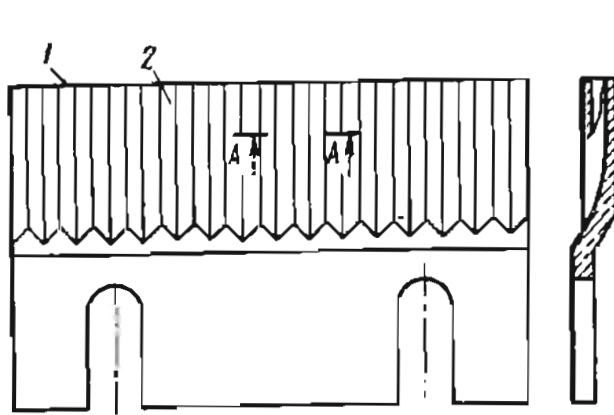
Схема безреберного ножа для центробежных свеклорезок
